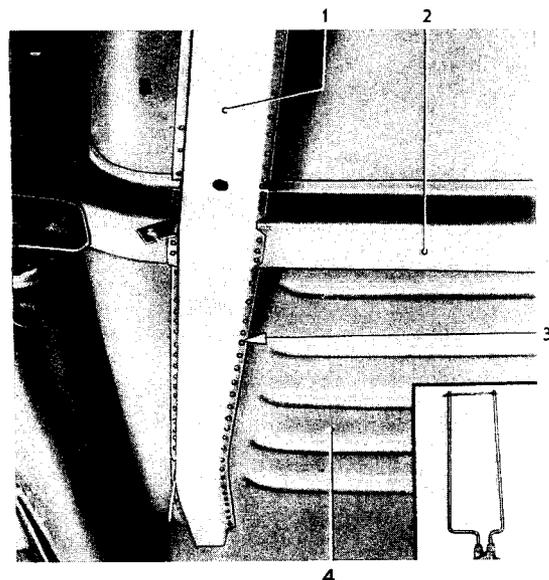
Linker Vorderrahmenlängsträger an Bodenblech und hinteren Motorquerträger punktschweißt – Rechten Längsträger in gleicher Weise punktschweißen
